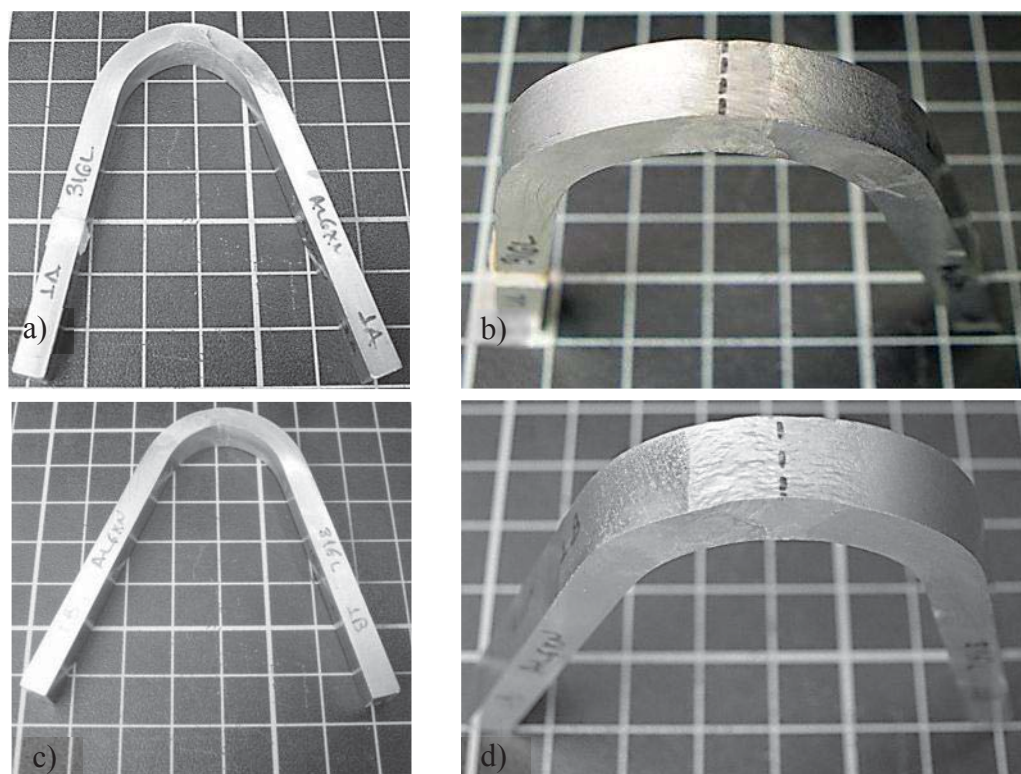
Imágenes de probetas de ensayo de doblez guiado: a-b) doblez para inspeccionar la soldadura de raíz, c-d) doblez para inspeccionar la soldadura de vista.
